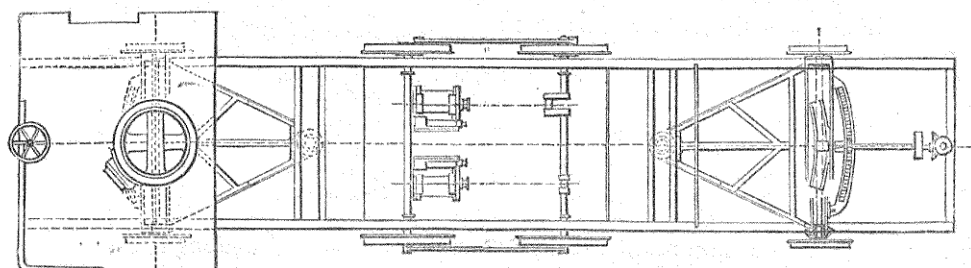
Car à vapeur de M. Perrett. Plan. Échelle 1/48.
